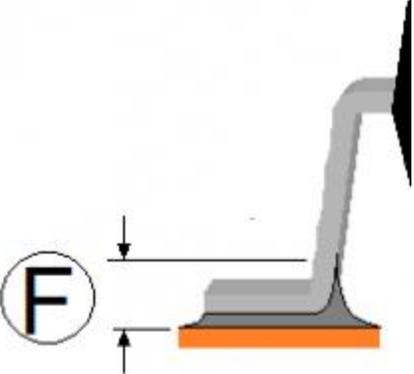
Criterios de inspección visual dimensional para componentes tipo ala de gaviota (gull wing) IPC 610
